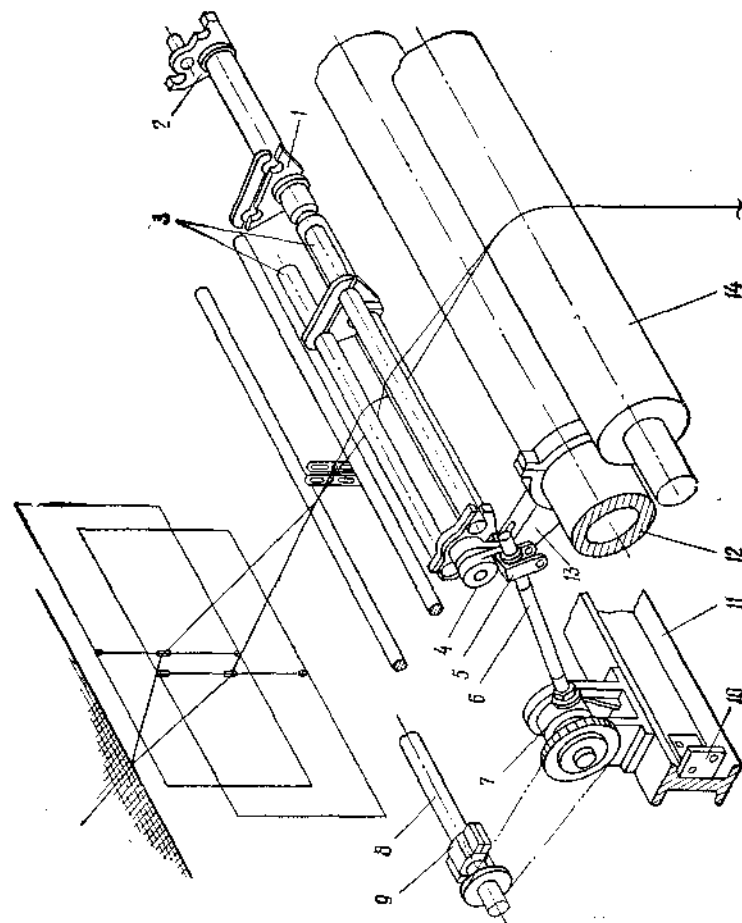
Ценовой уплотнитель станка СТБ-180-Л:
